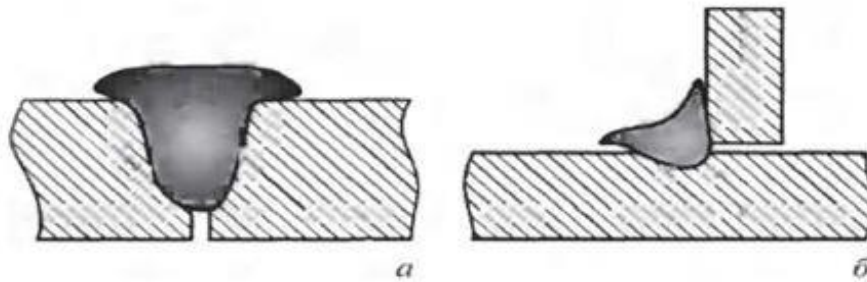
Наплыв в сварном стыковом (а) и угловом (б) соединениях
